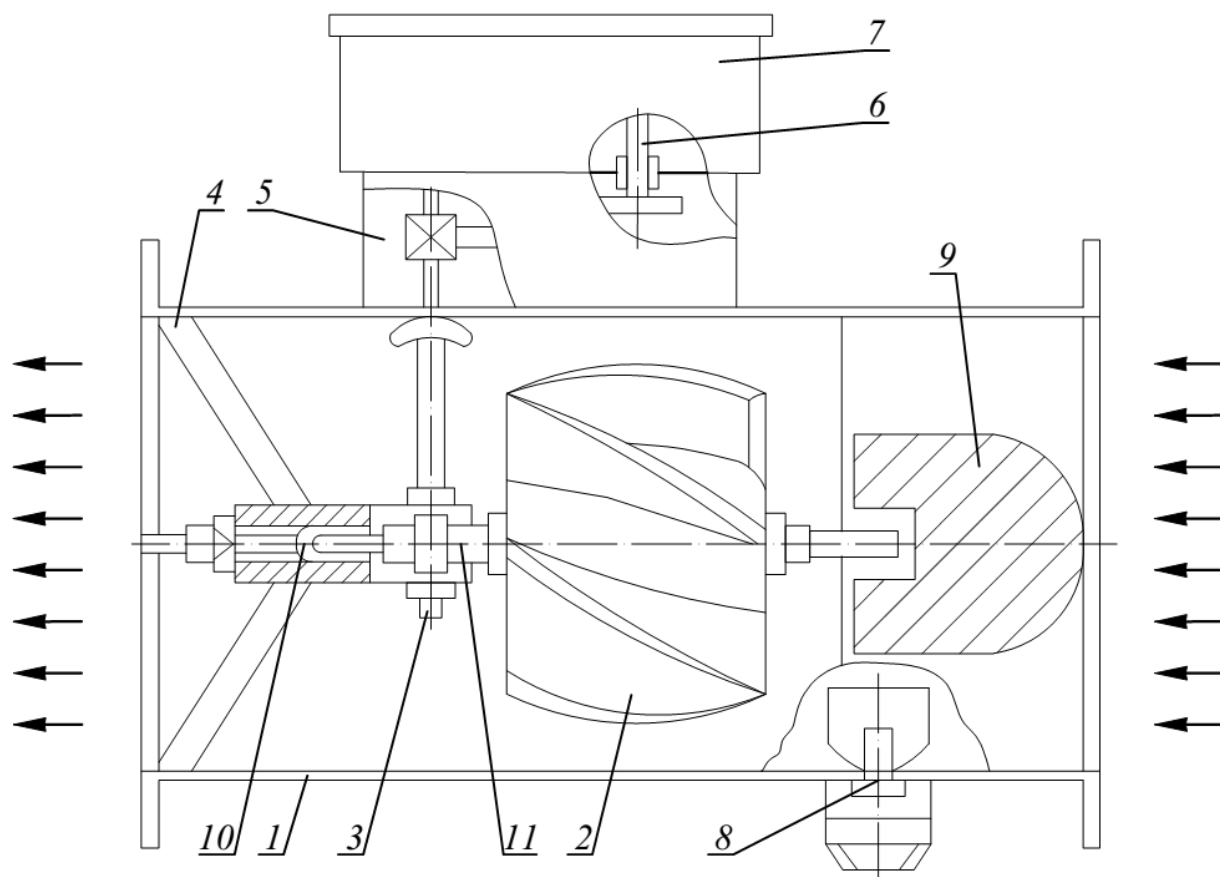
Схема скоростного счетчика с винтовой вертушкой: 1 – корпус; 2 – вертушка; 3 – передача; 4 – крестовина; 5 – передаточный механизм; 6 – счетный механизм; 7 – крышка; 8 – рычажный привод; 9 – струевыпрямитель; 10 – подшипник; 11 – ось вращения
